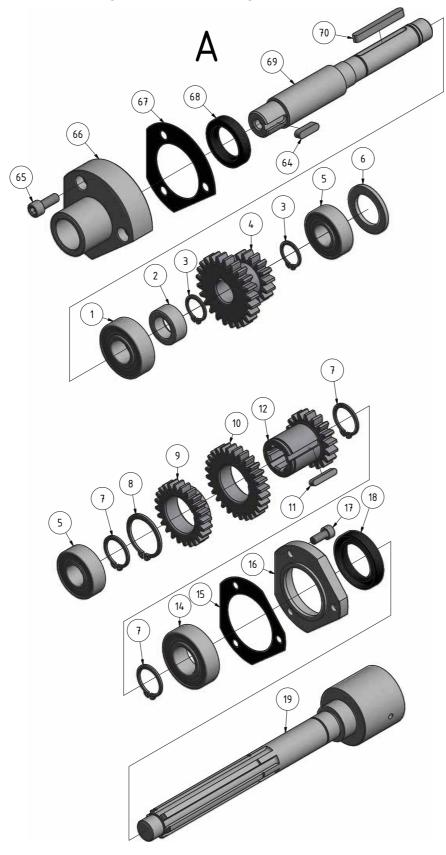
Vorschubgetriebe 3-6 - Feed gear 3-6
